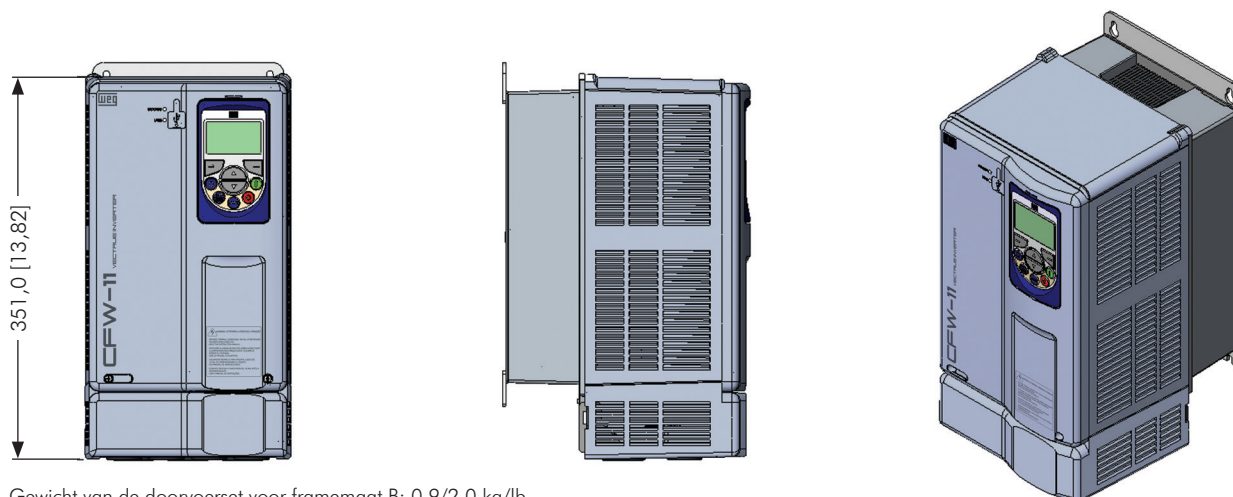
Afmetingen omvormer - framemaat D - mm [in]
